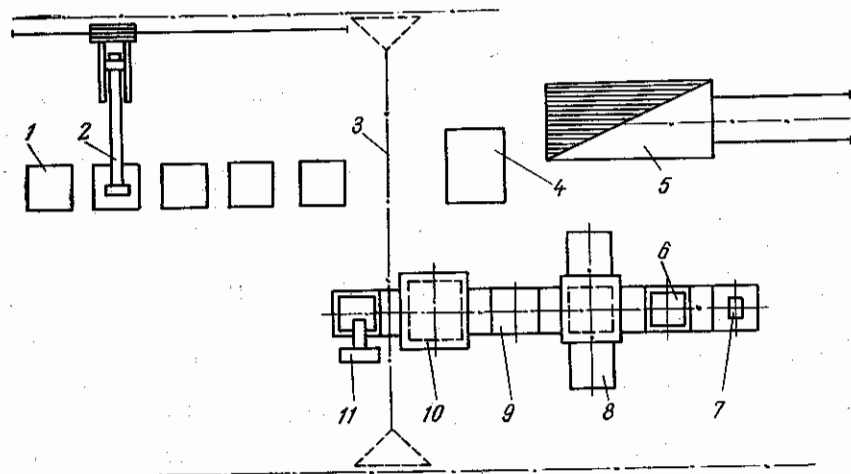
Линия изготовления стержней весом до 600 кг на базе пескомета:
